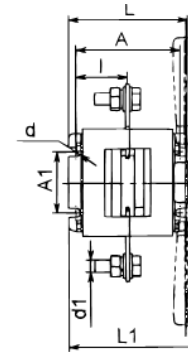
Б Выключатель-разъединитель на два направления однополюсный с боковой рукояткой
